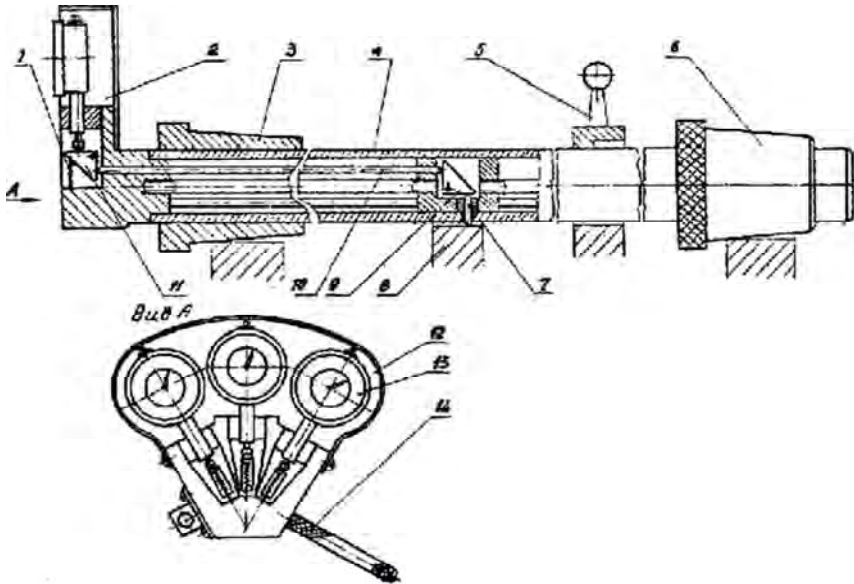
Приспособление для проверки несоосности гнезд под вкладыши коренных подшипников:
